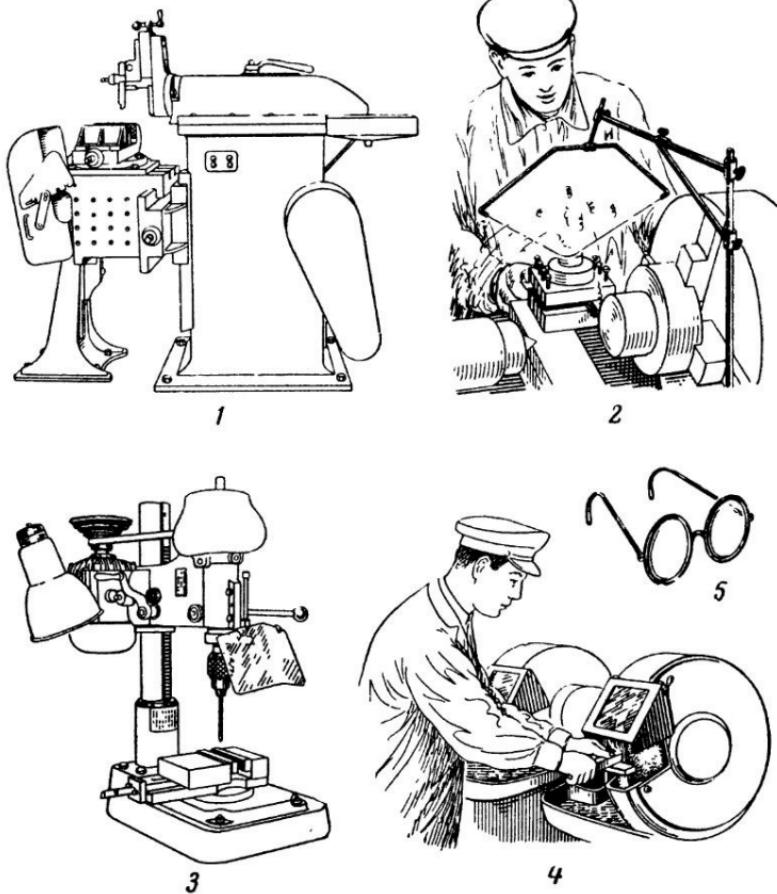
Приспособления для защиты от стружки при работе на станках: 1 — экран-стружкосборник для строгального станка; 2 — экран-отражатель для токарного станка; 3 — экран-отражатель для сверлильного станка; 4 — экран для электроточила; 5 — защитные очки.
